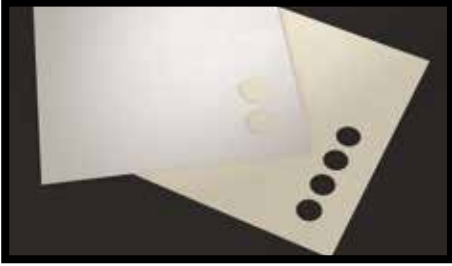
KERLITE, in allen Ausführungen, kann auch mit CNC-Maschinen gebohrt werden. Es sollte eine Vorbohrung mit einer Diamantbohrspitze erfolgen, die dann, falls notwendig, mit einem Fräser auf die gewünschte Größe erweitert werden kann. Eine Bohrspitze im Durchmesser zwischen 4 und 8 mm verwenden. Die Arbeitsgeschwindigkeit beträgt 40 mm/min. mit 900 Upm Spindelrotation. Mit diesen Werkzeugen empfiehlt sich. Die Ansatzstelle mit Wasser abzukühlen, die Bohrung mit niedriger Drehgeschwindigkeit zu beginnen, einen nicht zu starken Druck auszuüben und diesen auf jeden Fall je nach Festigkeit des zu bearbeitenden KERLITE Typs anpassen.
